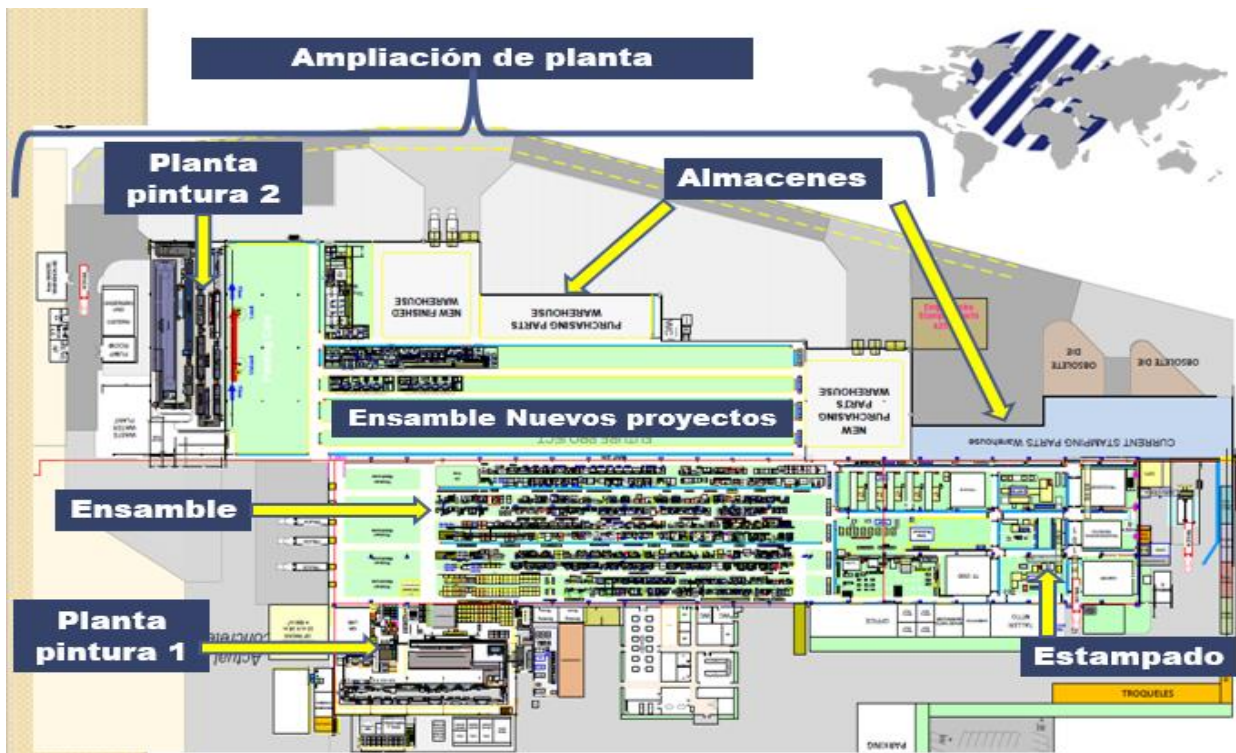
Lay Out de Planta Yorozu Y-MEX
